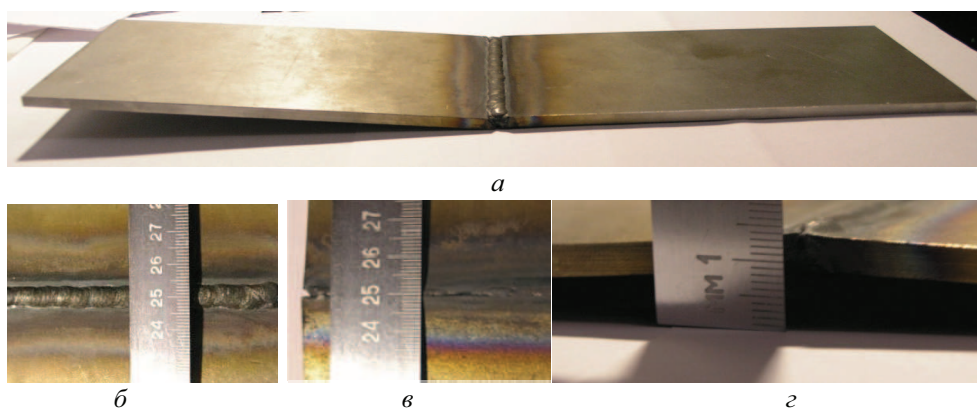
Фотографии пластин после сварки: а – общий вид, б – поперечный размер шва и расстояния до полос побежалости со стороны наложения шва, в – то же с обратной стороны пластины, г – стрела прогиба пластины после остывания шва
